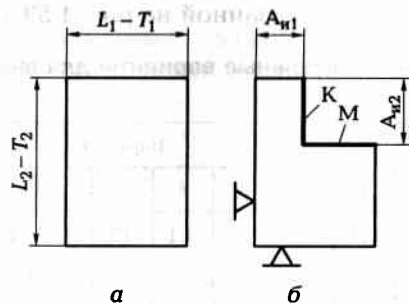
Схема базирования заготовки (а) при обработке (б) двух поверхностей
